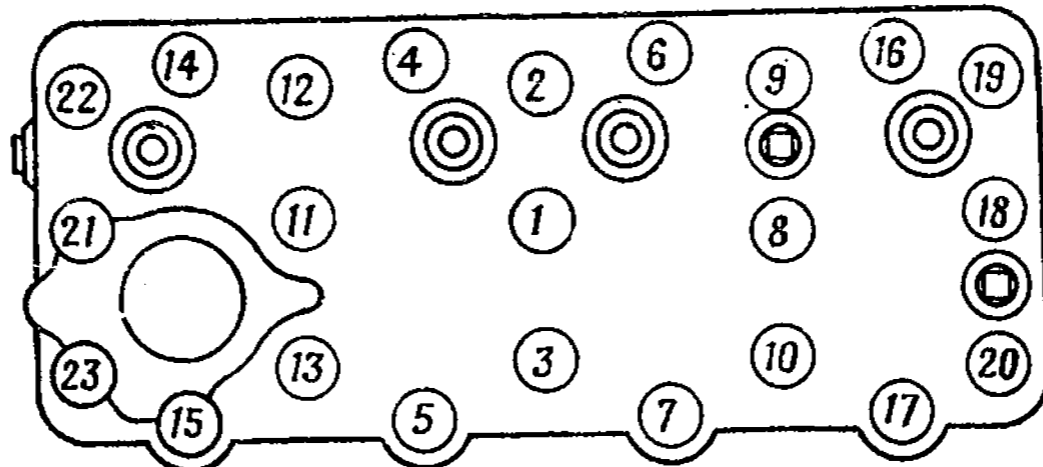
Порядок затяжки гаек головки блока цилиндров:
